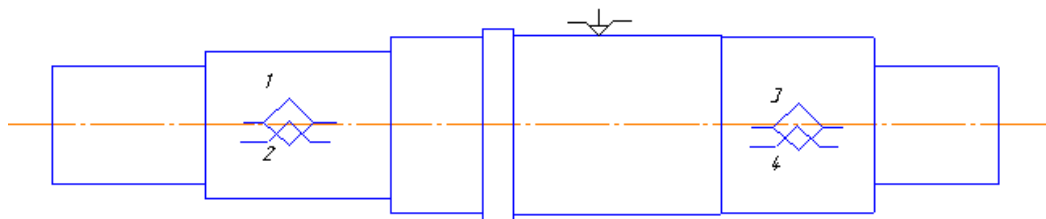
Схема базування заготовки при фрезерно-центрувальній операції
